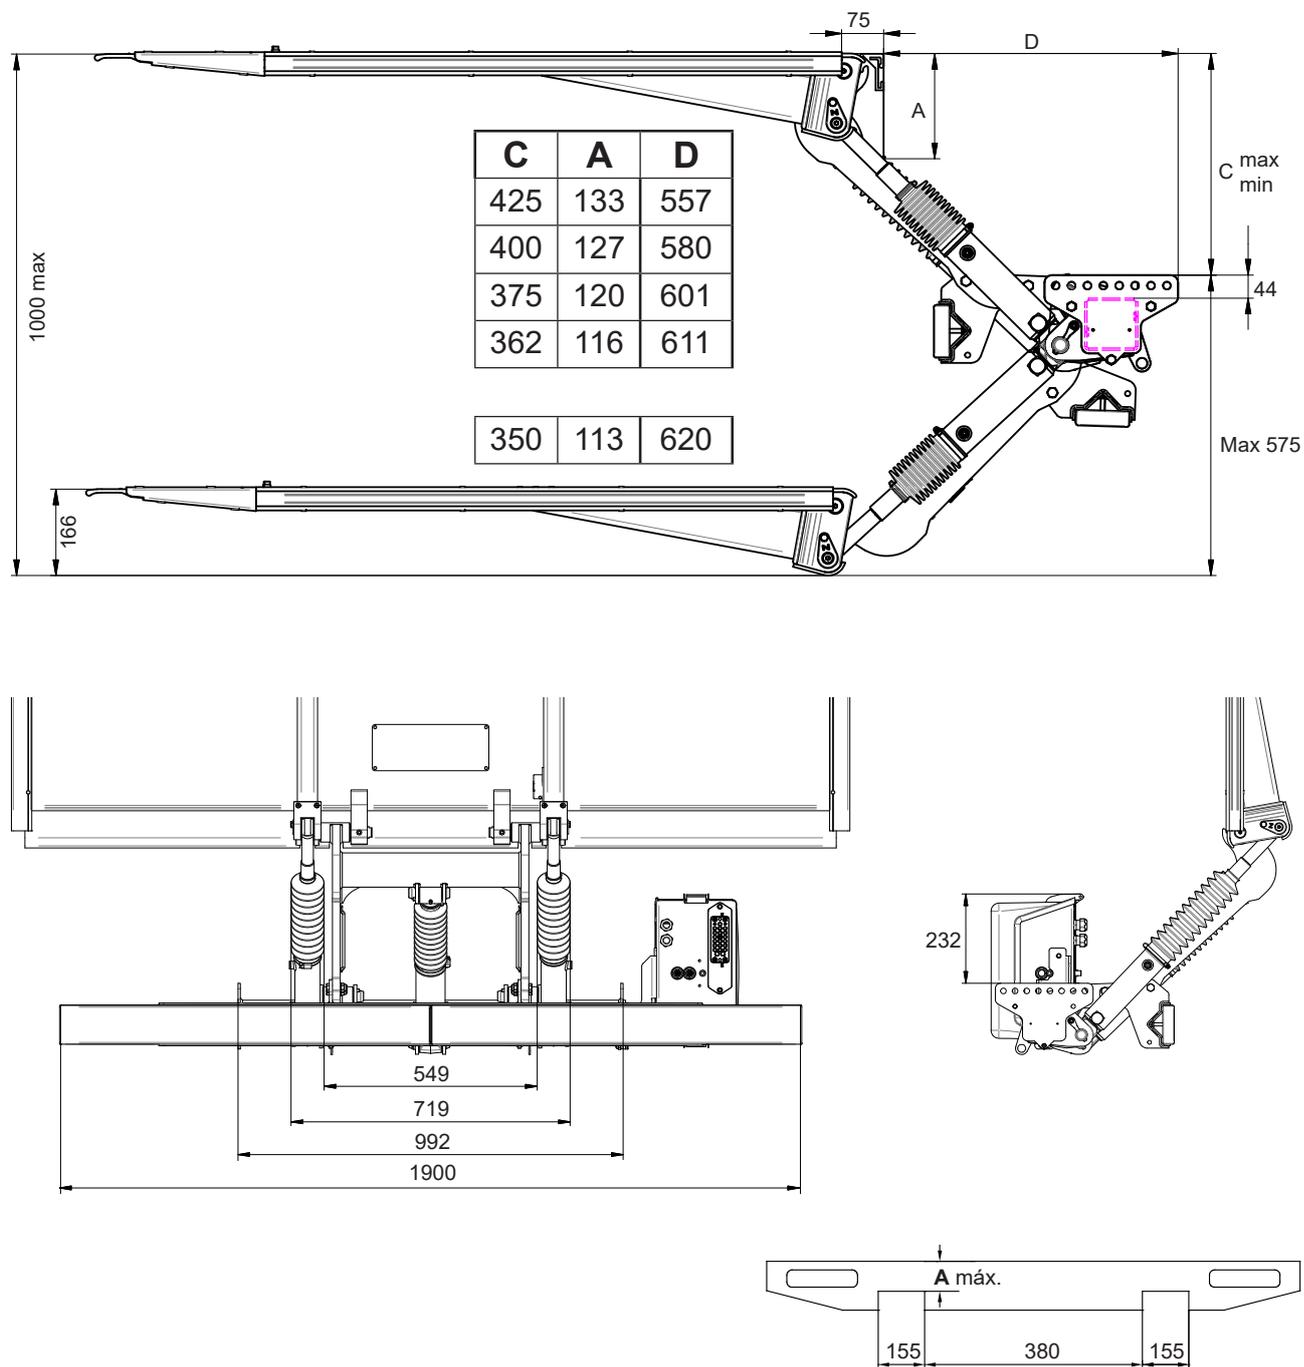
Dimensiones de montaje para Z3N(U) 75-100
